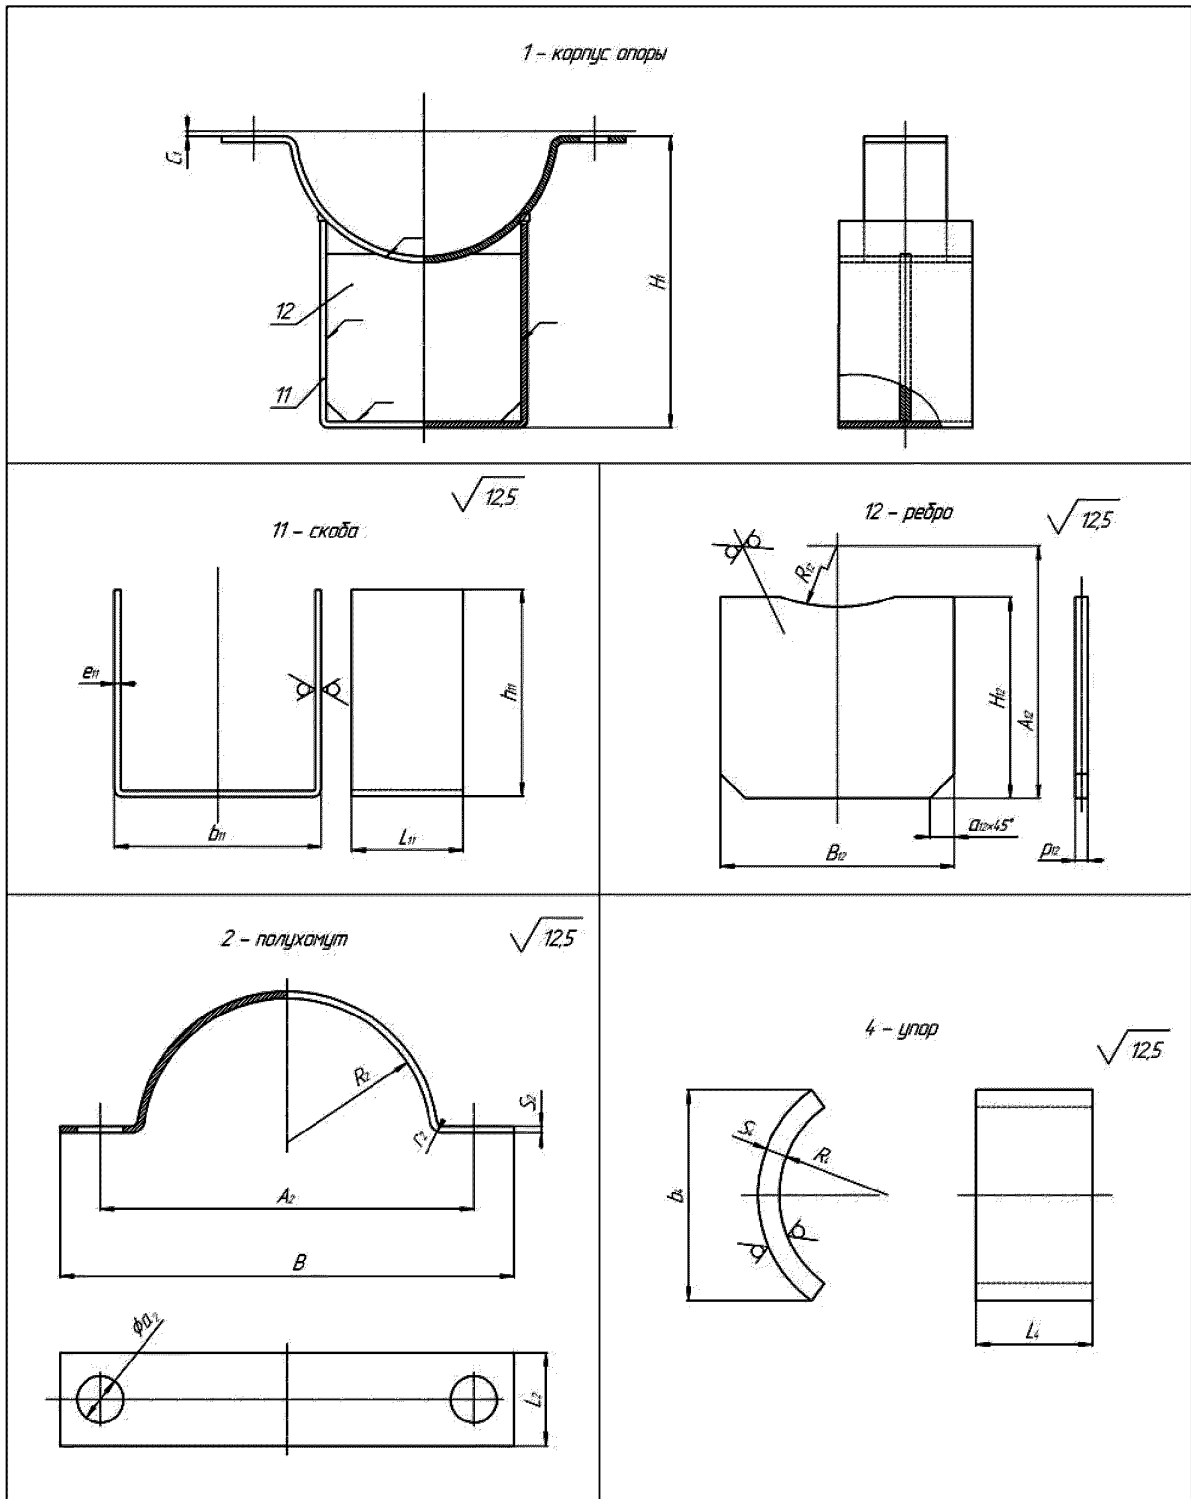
Детали изделий 01-XXXX-F-1C-03-A,
